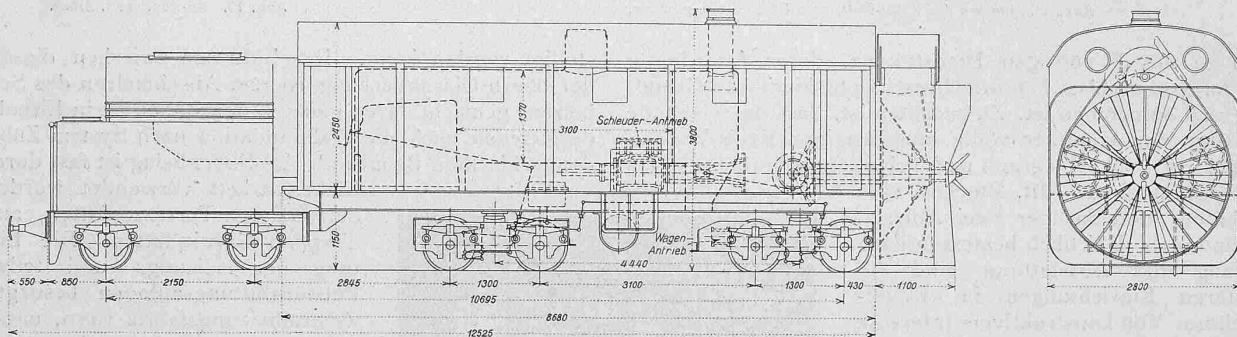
Schneeschleuder-Maschine der Rh. B., gebaut von der Lok.-Fabr. Winterthur. — 1 : 100. — Leergewicht 36,9 t + 6,6 t (Tender); Dienstgewicht 49,6 + 16,6 = 57,2 t; Heizfläche mit Ueberhitzer 110 m²; Wasser im Kessel 3350 l, im Tender 7500 l, Kohlen 2,5 t.
